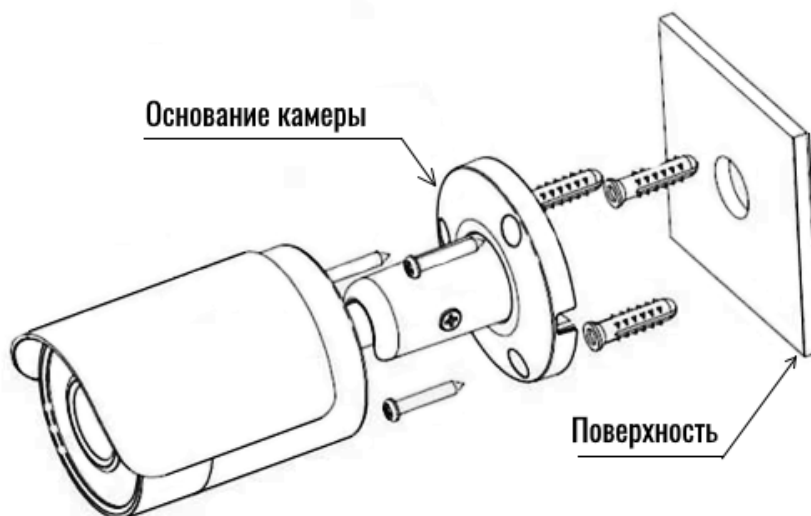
Схематичное изображение монтажа цилиндрической АHD видеокамеры.
